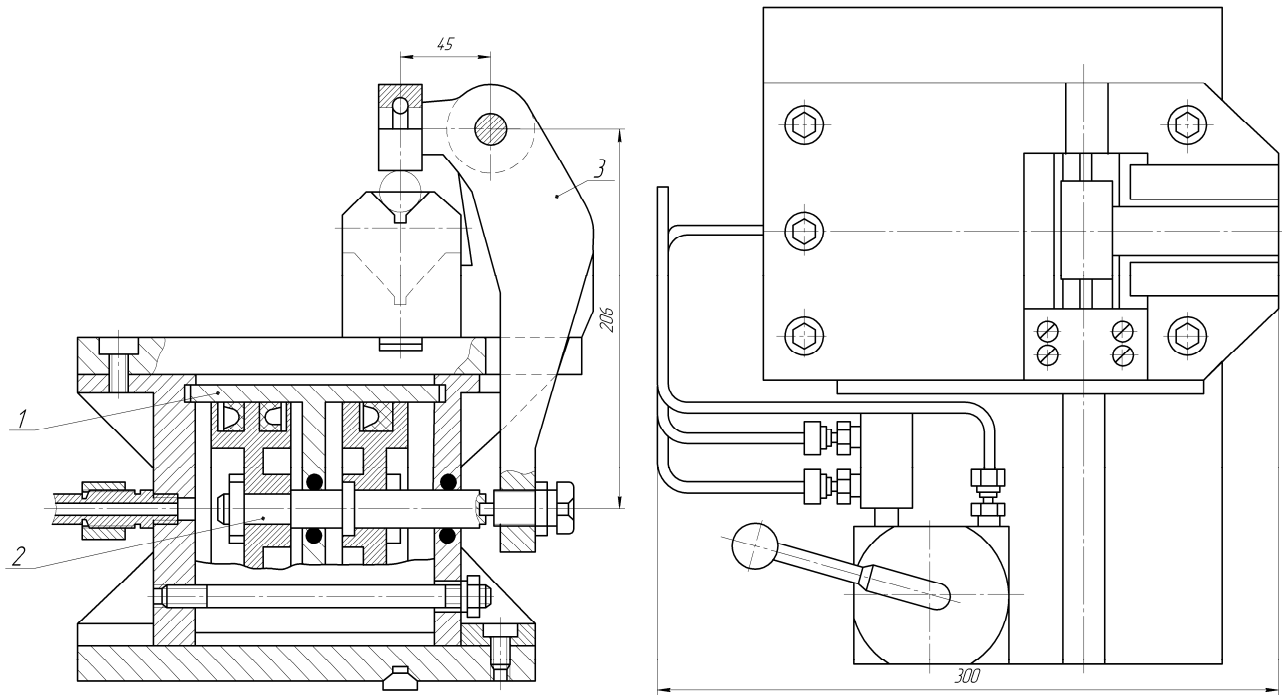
Будова й параметри пристрою для фрезерування деталей типу валика
